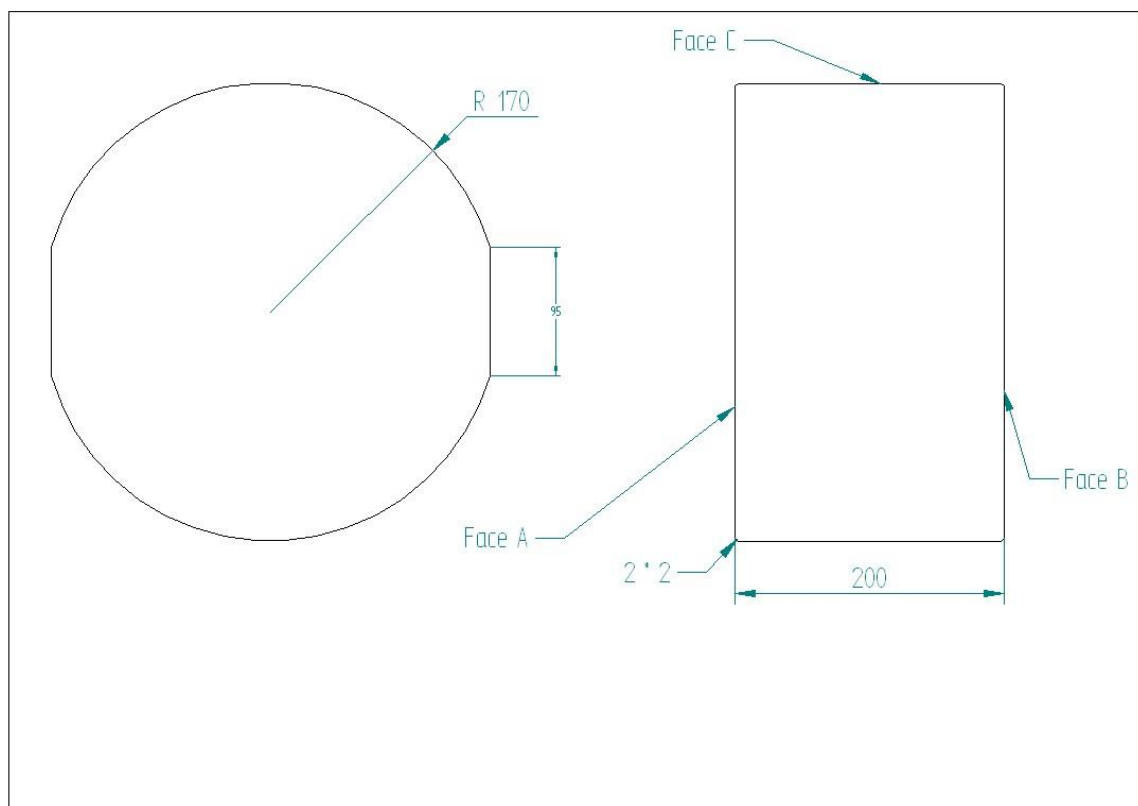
Plan d'un substrat cylindrique type Adv. VIRGO
